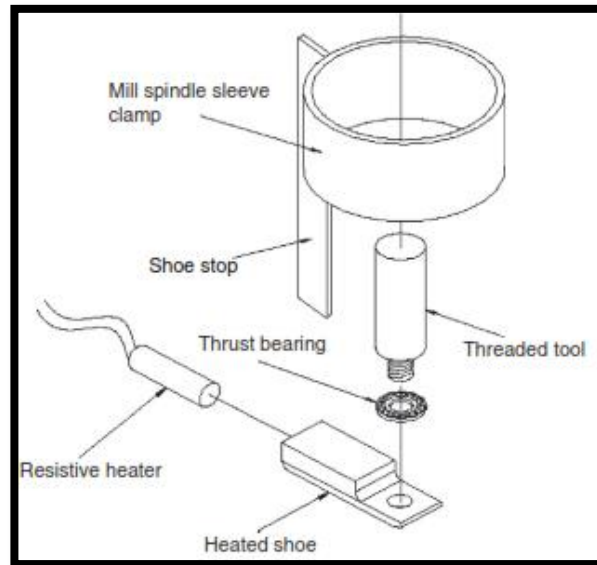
Proceso de soldadura por fricción agitación
